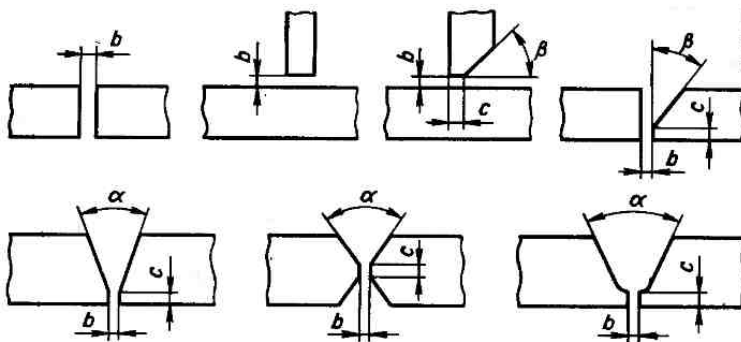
Конструктивные элементы разделки кромок и сборки кромок под сварку
